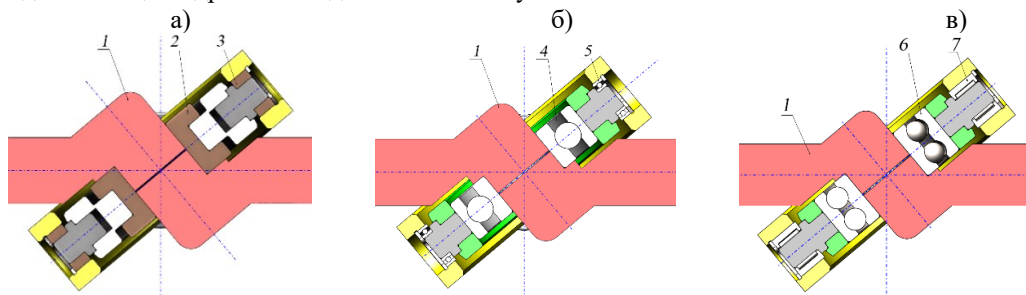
Конструктивні схеми кривошипно-повзунного механізму оборотного ПНР на основі:
